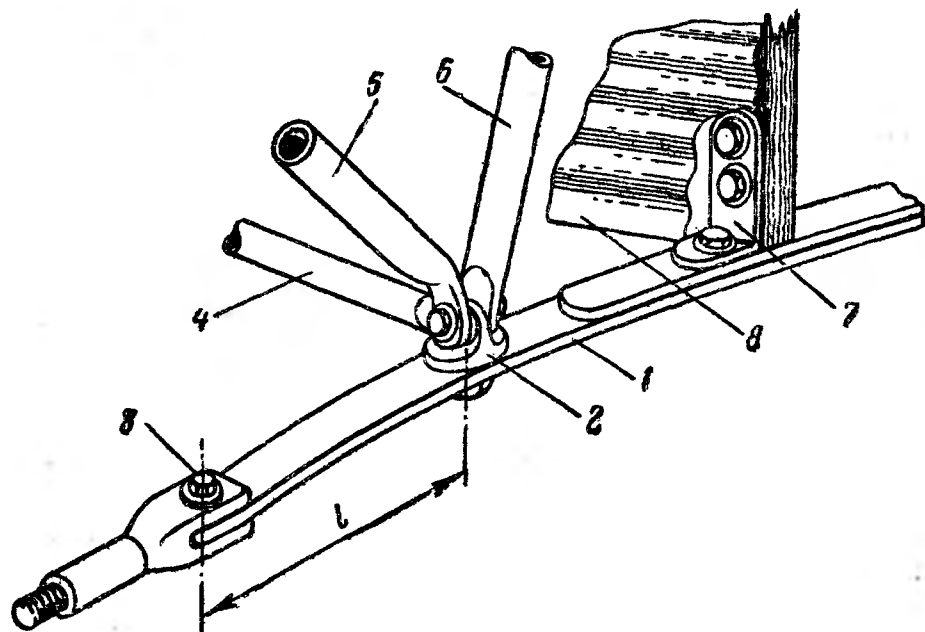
Задняя подвеска на аэросанях конструкции Ф. М. Маслова: 1 — рессора; 2 — ушко; 3 — осевой палец; 4 — разгрузочный подкос; 5 — труба ограждения винта; 6 — распорная труба; 7 — угольник крепления рессоры к корпусу; 8 — корпус.
